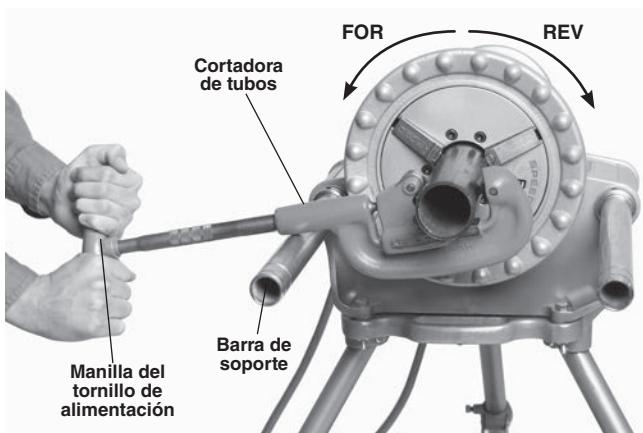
Corte de un tubo con una cortadora manual; rotación de la máquina (la cortadora debe mantenerse en contacto con la barra de soporte)
